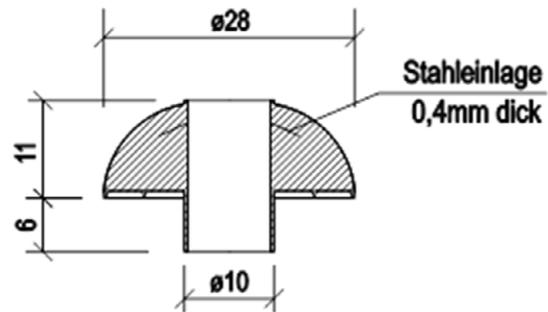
Pilzkopfdichtung aus Kunststoff mit Stahleinlage für die Sechskant-Holzschraube nach Bild 2.1 und für Stahlhaken
